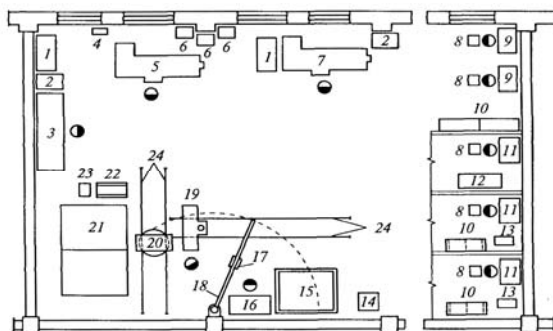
Примерная планировка сварочно-наплавочного участка:
